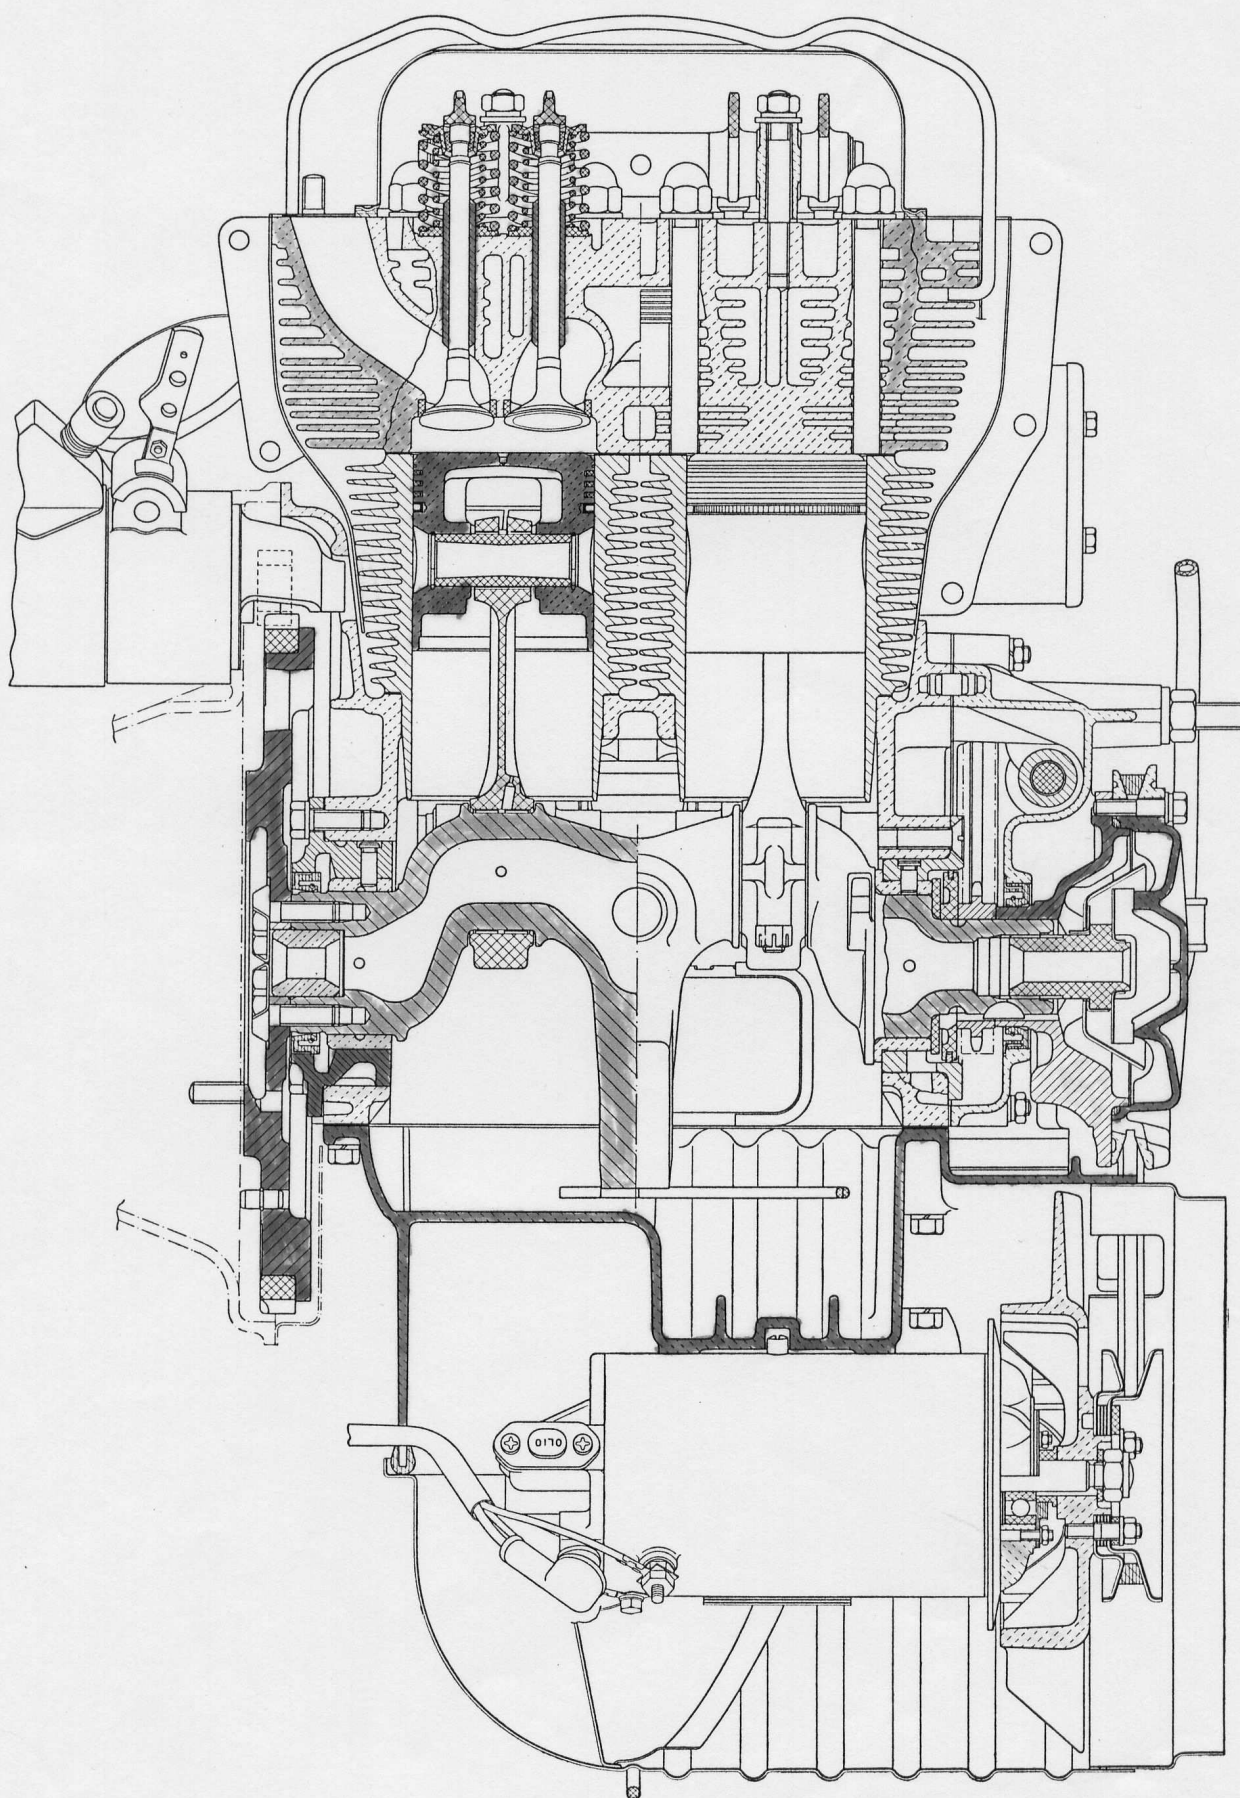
Schnitt durch die Zylinder und die Kurbelwelle.
